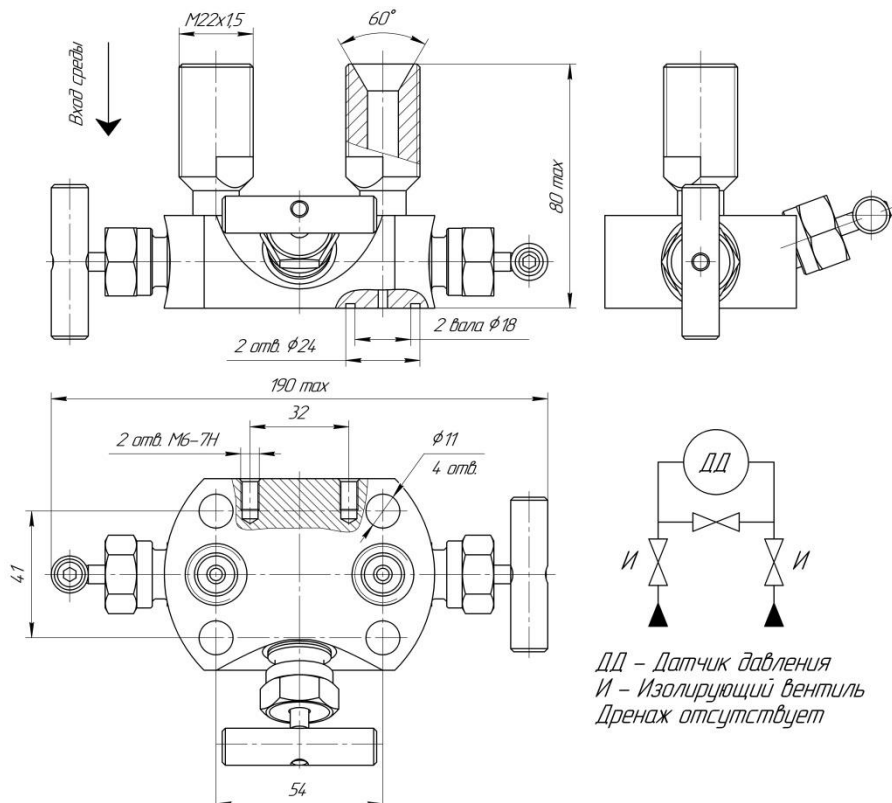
Габаритно-присоединительные размеры и гидравлическая схема 3-вентильных блоков исполнения БКНЗ-11-20П2
